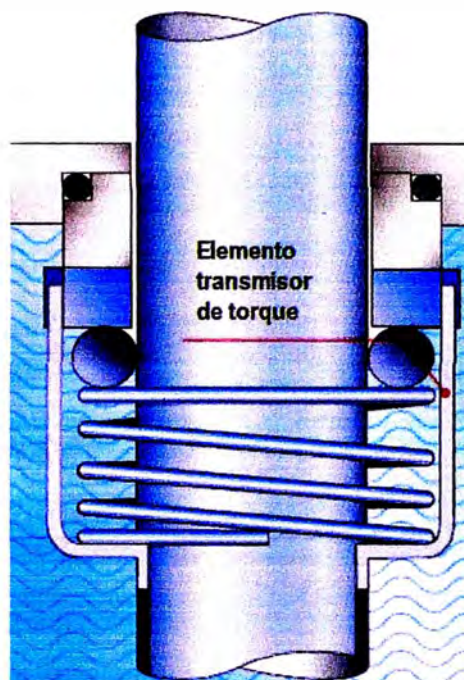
El elemento de transmisión de torque completa la lista de componentes del sello mecánico.
